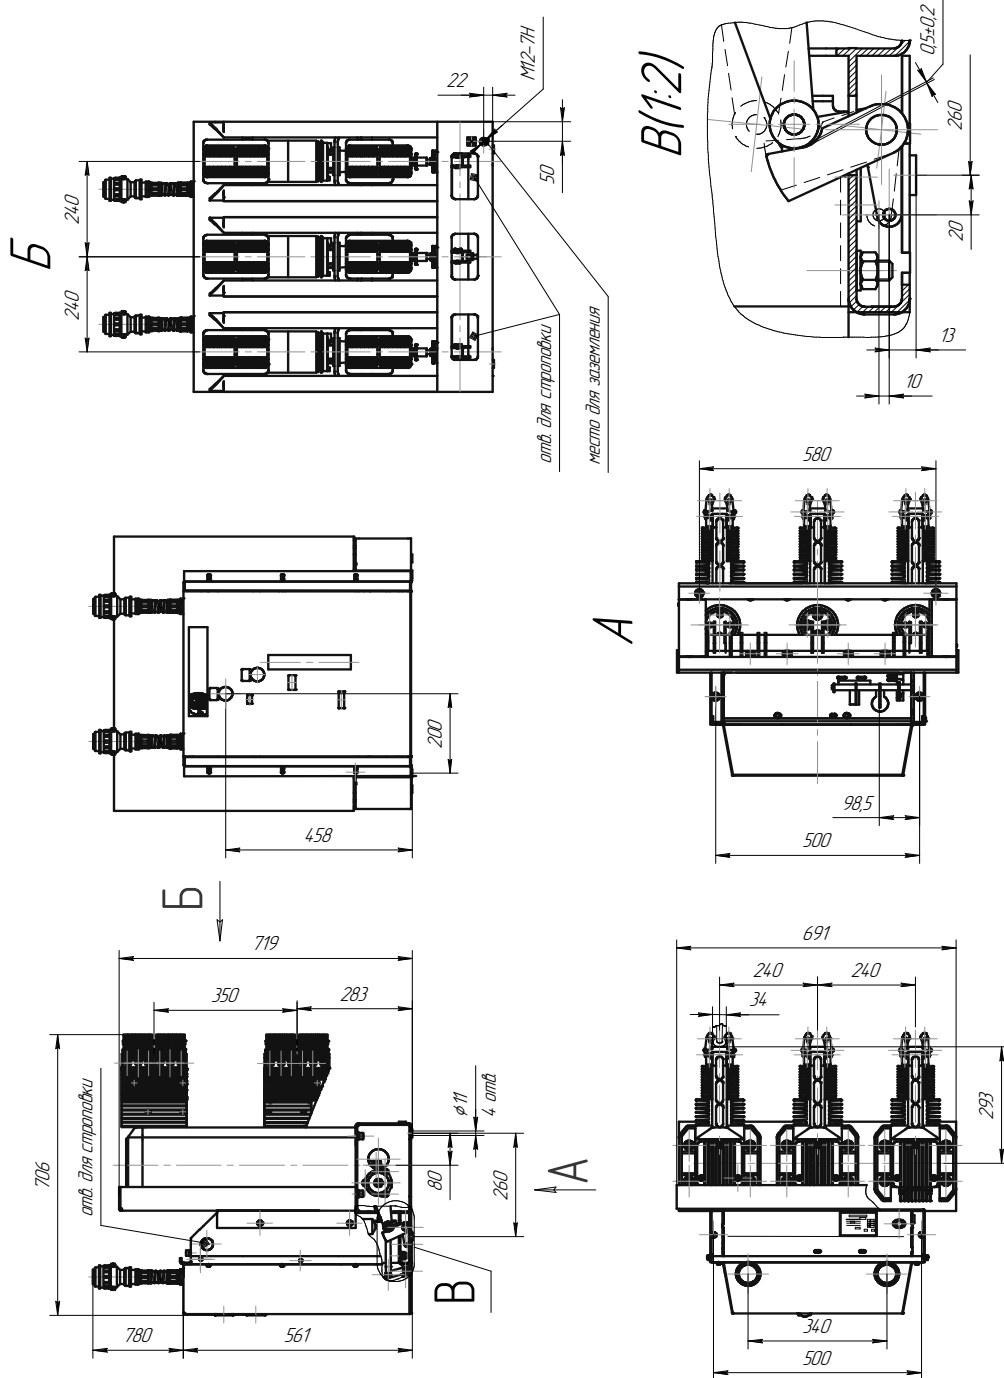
Габаритные, присоединительные и установочные размеры выключателя типа ВВУ-СЭЦ-Г-10-31,5(40)/3150(2000,2500)
